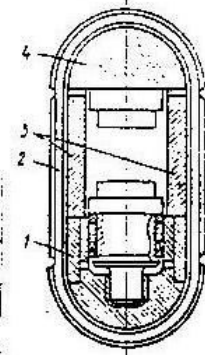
Схема прес-са со станиной, скреп-ленной обмоткой из высокопрочной ленты
